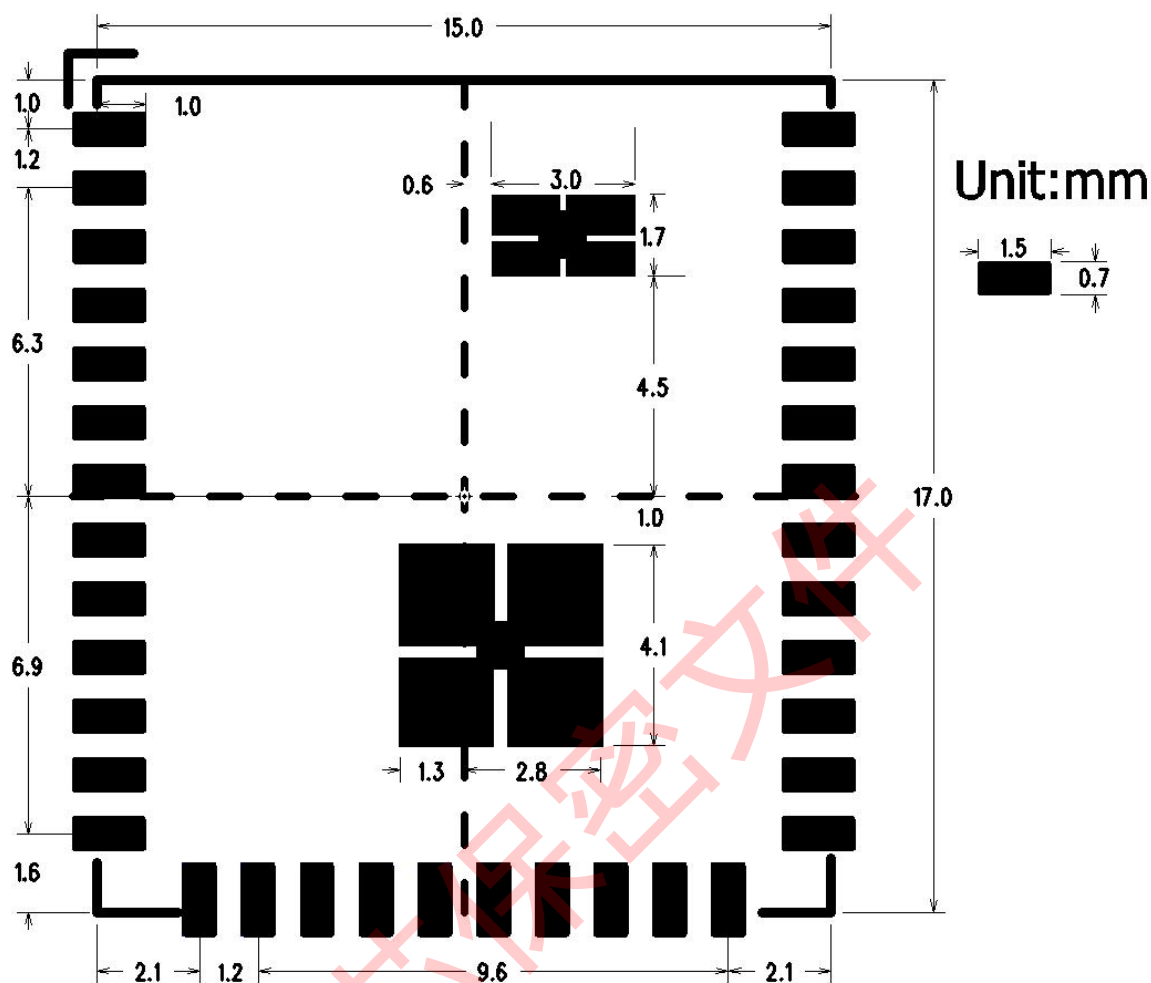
TX-AH-Rx00Pxx模组PCB封装图
